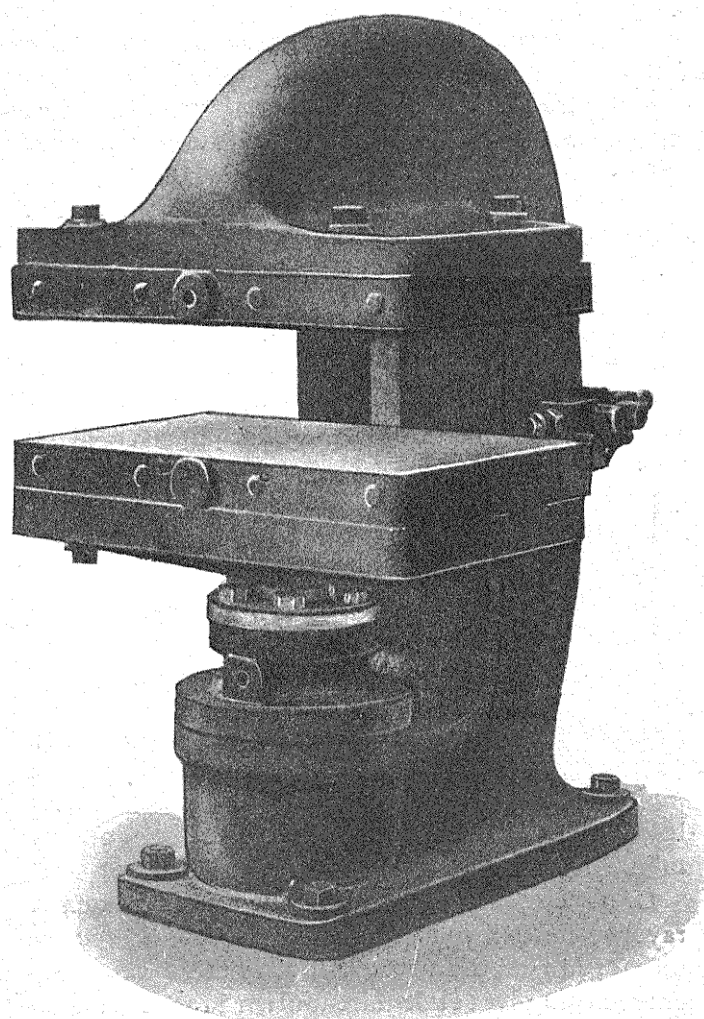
Presse hydraulique à mouler les petites pièces.
